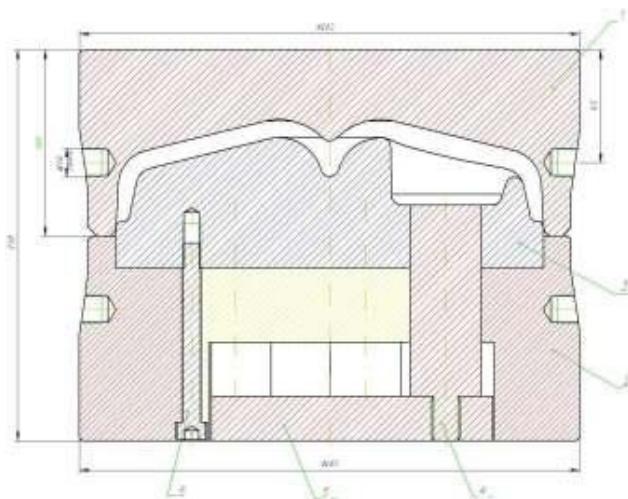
Схема штампа для объемной штамповки медного венца фурмы: 1-матрица; 2-обойма; 3-пуансон; 4-выталкиватель
